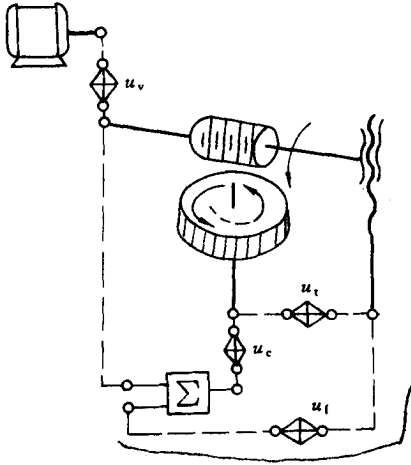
加工斜齿圆柱齿轮时滚齿机传动原理图
